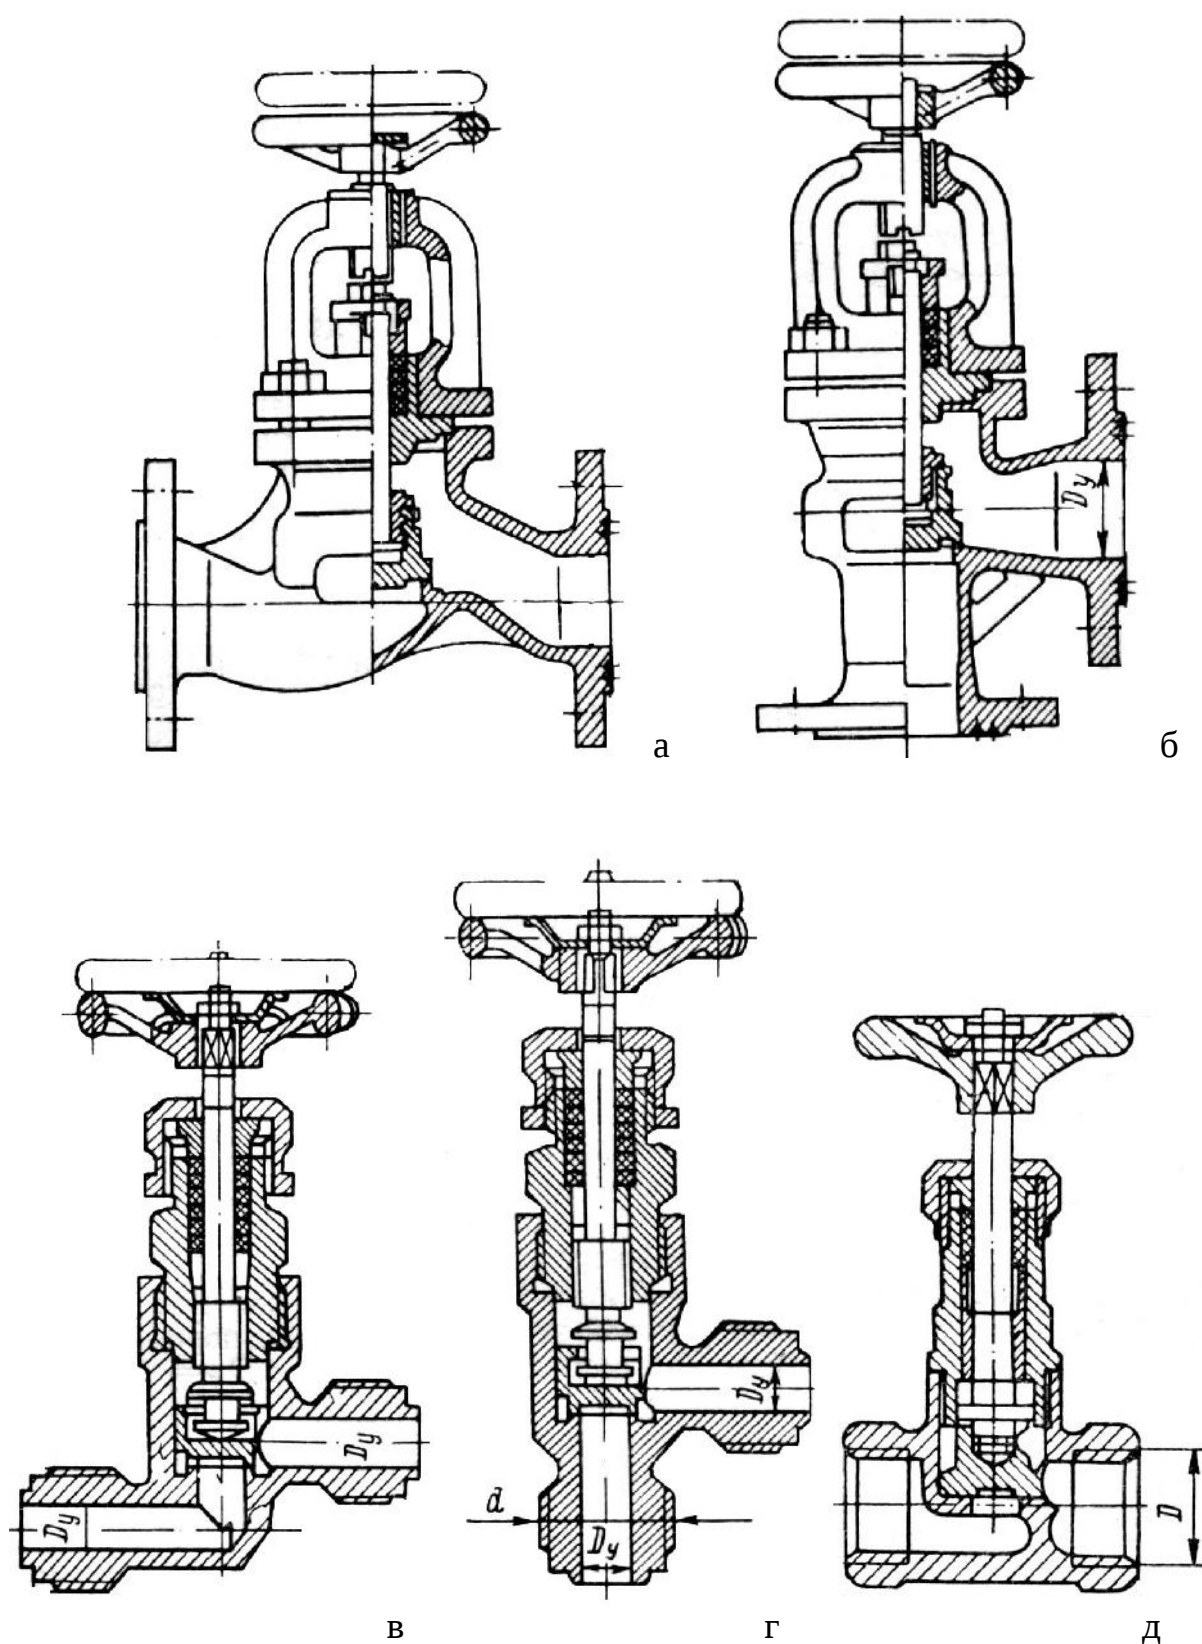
Запорные клапана: а – проходной запорный фланцевый клапан; б – угловой запорный фланцевый клапан; в – проходной запорный штуцерный клапан; г – угловой запорный штуцерный клапан; д – проходной запорный муфтовый клапан
